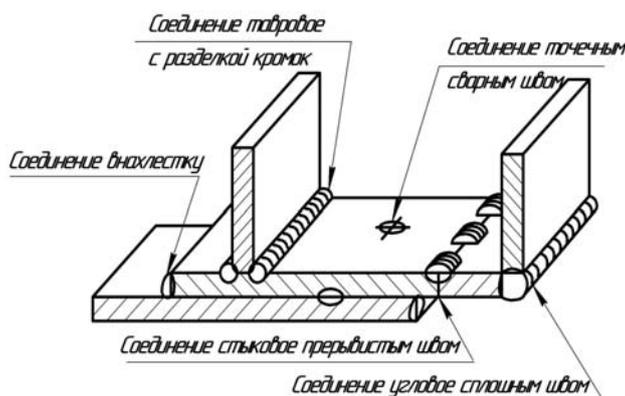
Типы сварных соединений и швов
